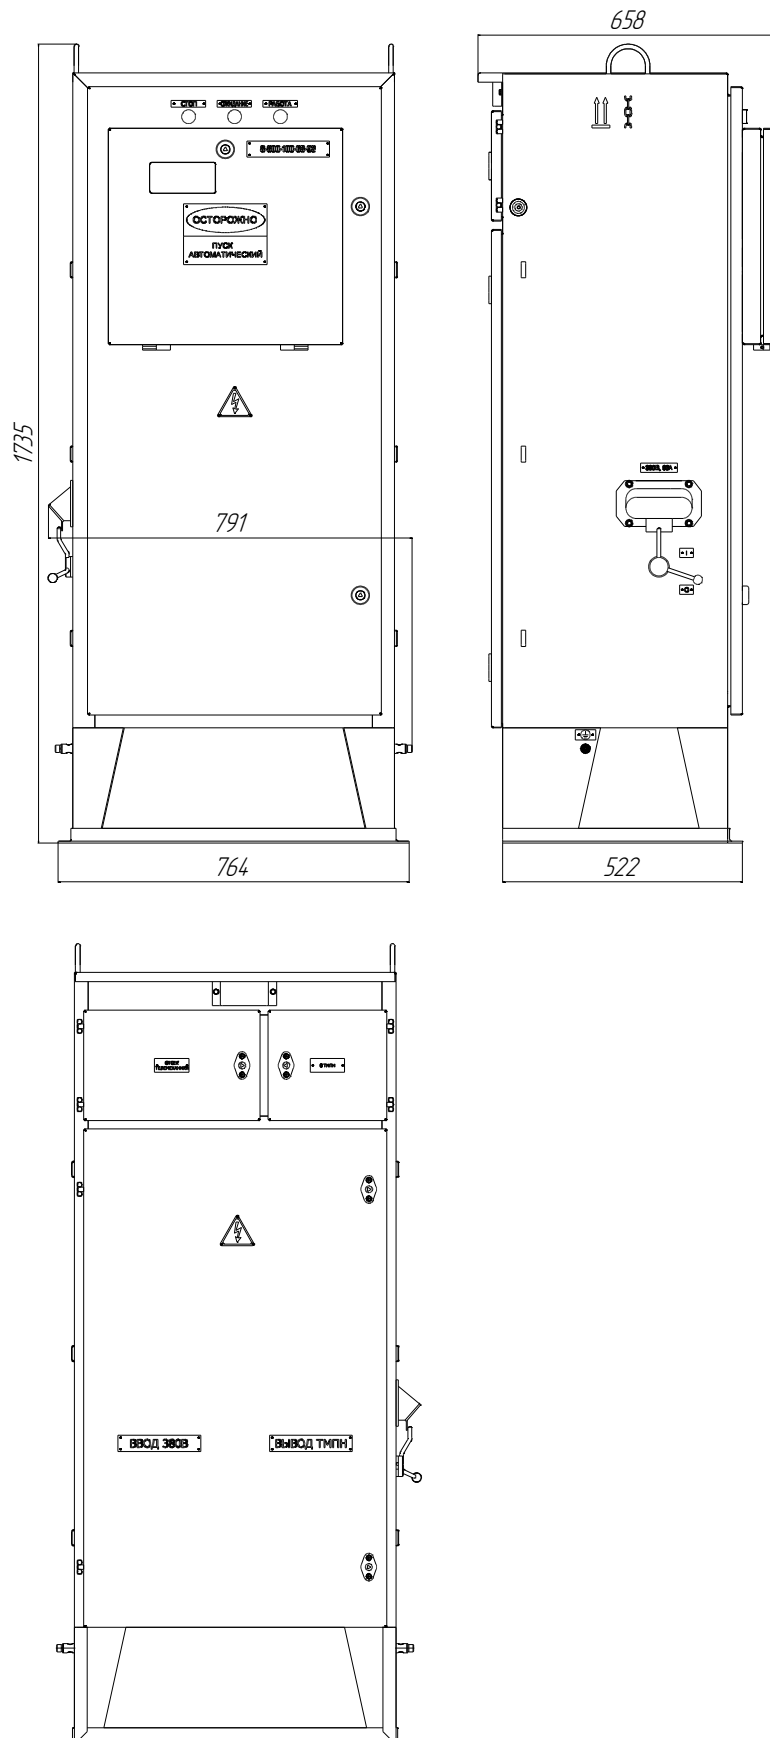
Внешний вид и габаритные размеры СУ ИРЗ-700
